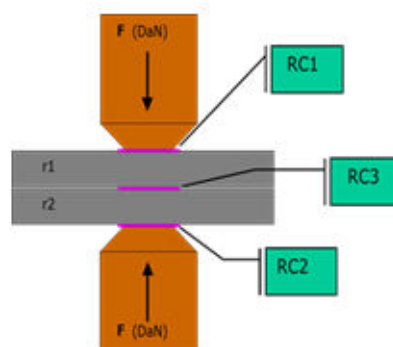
Mécanisme de formation de point de soudure de soudage par point
